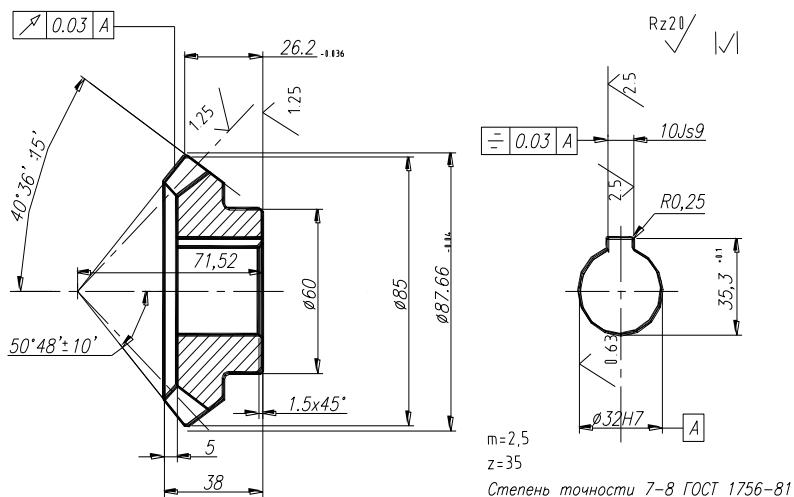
Зубчатое колесо коническое. (Сталь 45).
